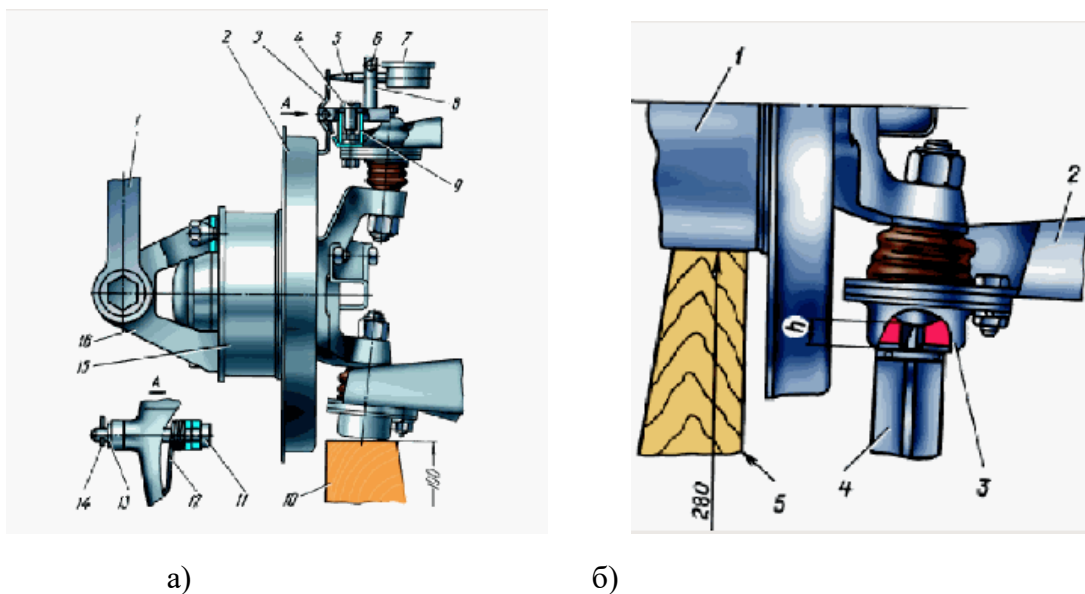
Схема проверки шаровых шарниров механическим способом:
